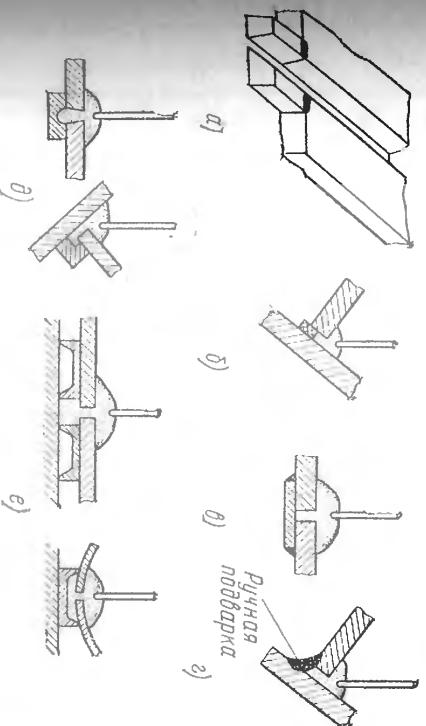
Подготовка заготовок к сварке под флюсом с использованием начальных и выводных планок (а), асбестовой набивки (б), оставающейся стальной подкладки (в), предварительной ручной подварки (г), флюсомедной подкладки (д), флюсовой подушки (е)
